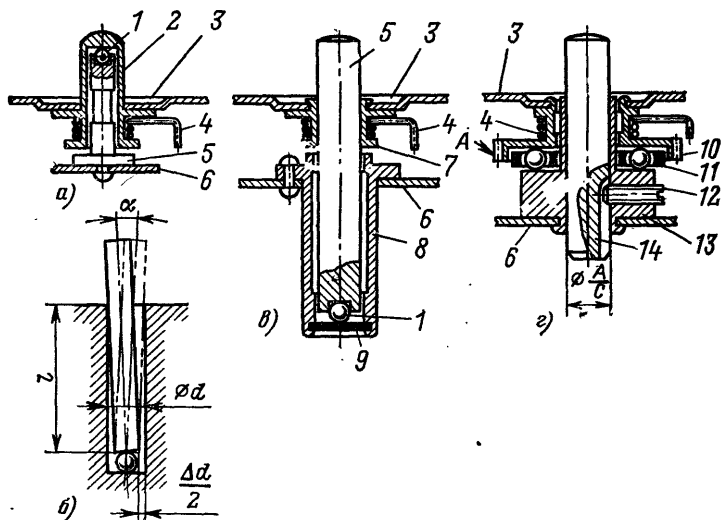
Конструкция шпиндельного узла диска ЭПУ (А — зубчатый венец ведущей шестерни автоматического ЭПУ).
